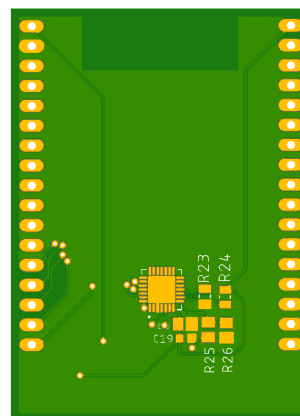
Vista inferior PCB (Font: Ernest Porqueras)
